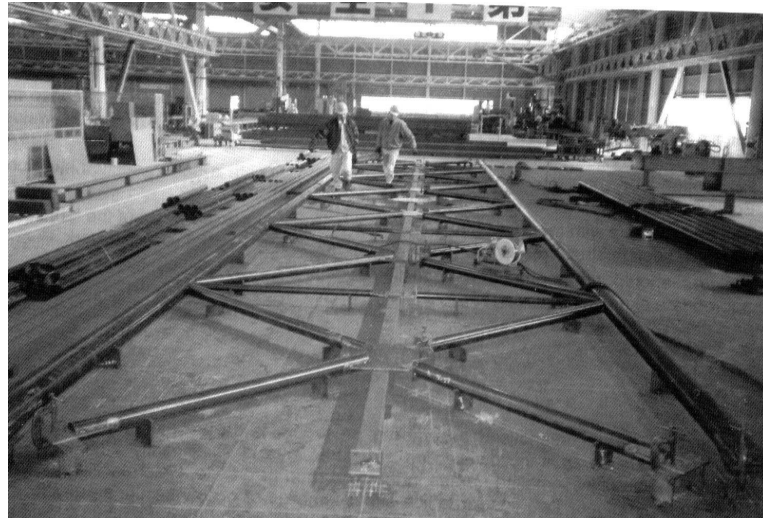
Gabarito para uma viga do tipo Howe
